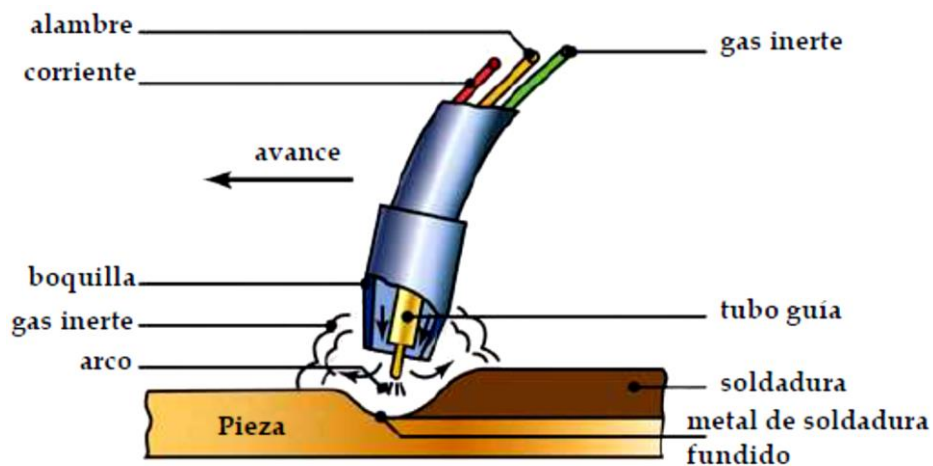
Esquema de soldadura por sistema MIG
